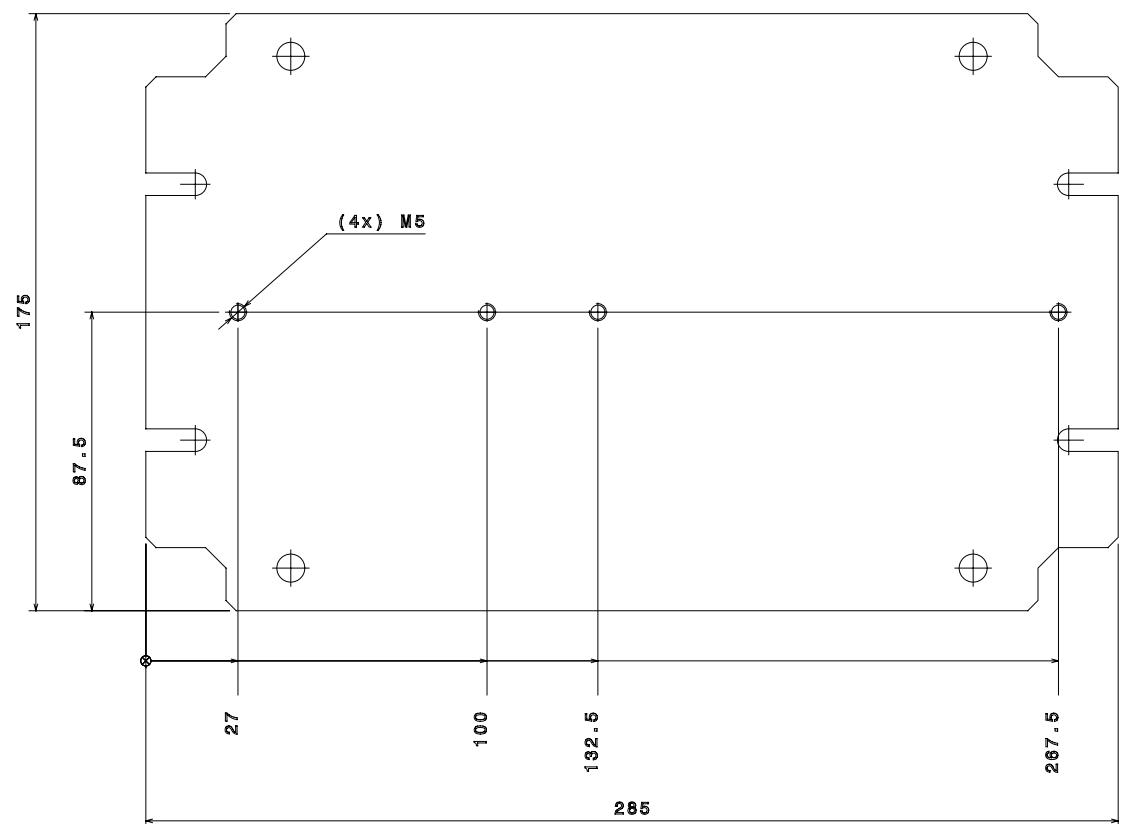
/1	Designation: piece, sous ensemble ou ensemble . Description: part, sub assembly or assembly.	Material KL1603.510
